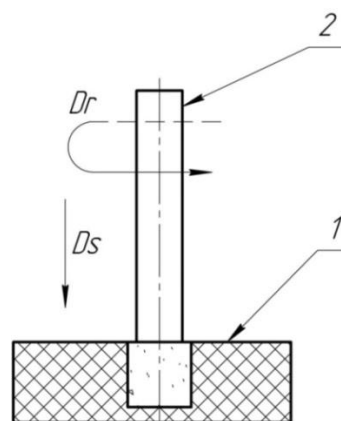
Схема правки алмазных кольцевых сверл абразивными брусками
